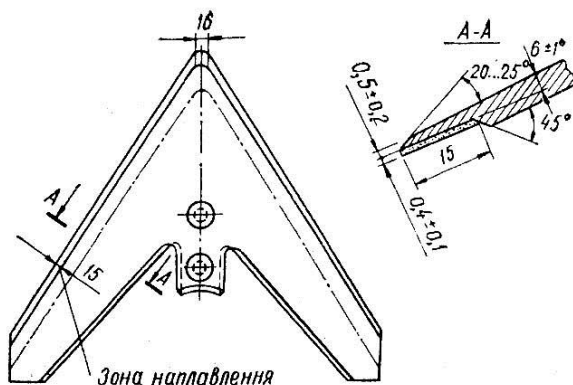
Підготовка лапи культиватора до наплавлення.
